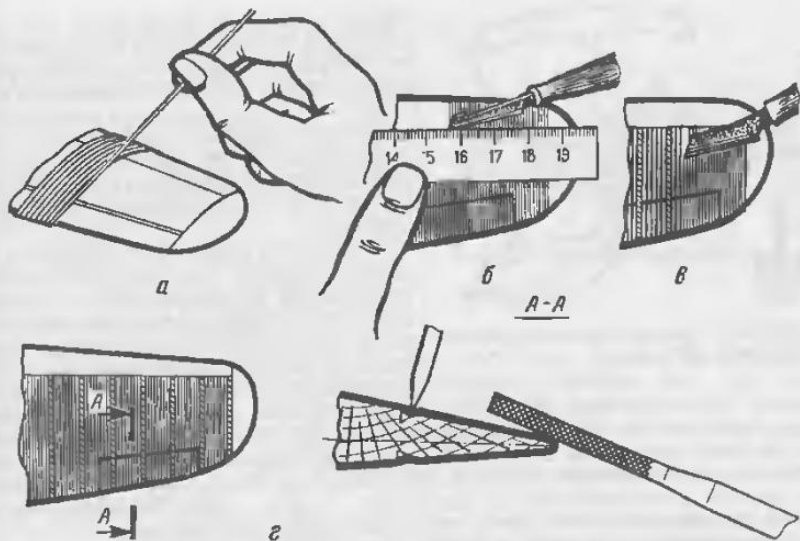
Процесс изготовления гофрированной обшивки. Самолет Р-11 (Польша): а - плотная укладка проволоки; б - обрезка; в - прорезивание; г - прокатка по лобуку элерона, обработка задней кромки
